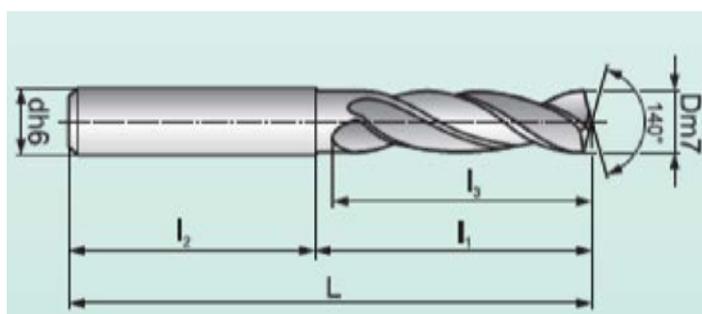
Сверло цельное твердосплавное – размеры указаны неверно
